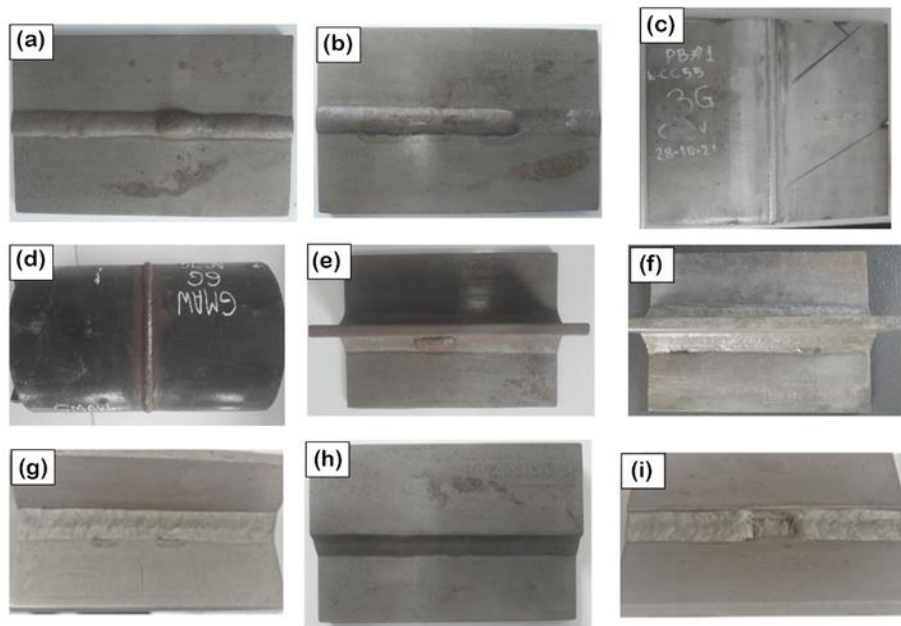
Probetas soldadas utilizadas, (a-d) soldadura de ranura juntas a tope, (e-g) soldadura de filete para juntas en T, (h, i) soldadura de filete para juntas de traslape
